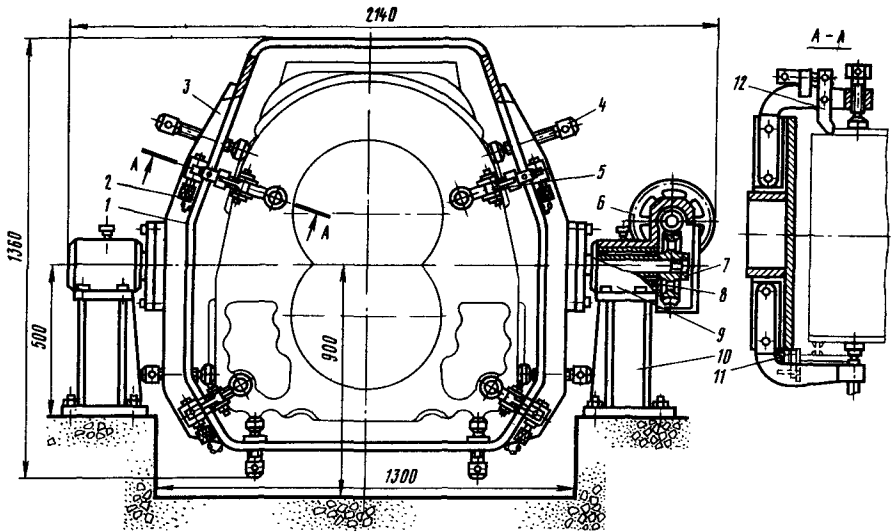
Стенд-кантователь для разборки и сборки воздуходувки дизеля 2Д100:
